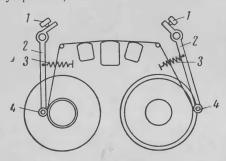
Конструкция автоматического устройства, управляющего направлением движения магнитной ленты при намотке ее на сердечники.
